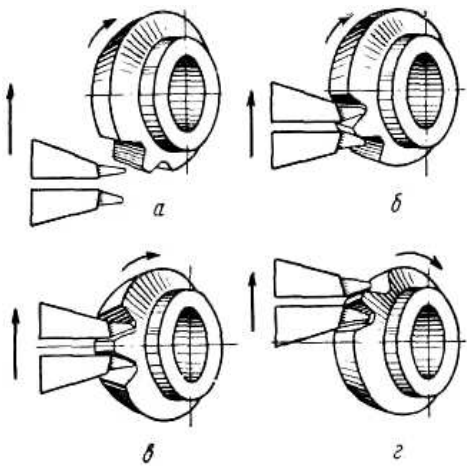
Схема образования зубьев Рис. 3.29. Исполнительный механизм группы Φ_v
